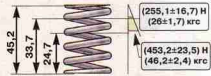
Основные данные для проверки наружной пружины клапана
